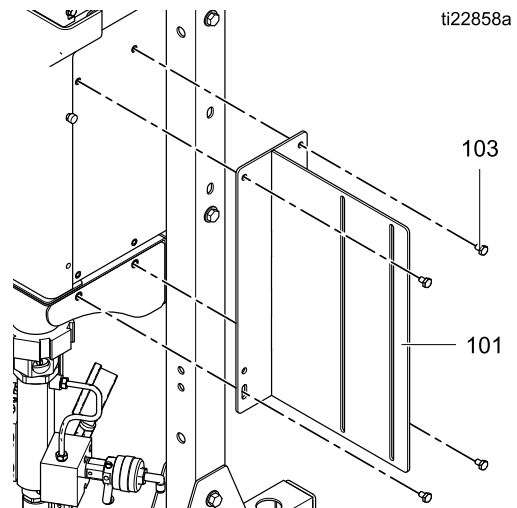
Detalle de las conexiones de cable de la placa de aislamiento
